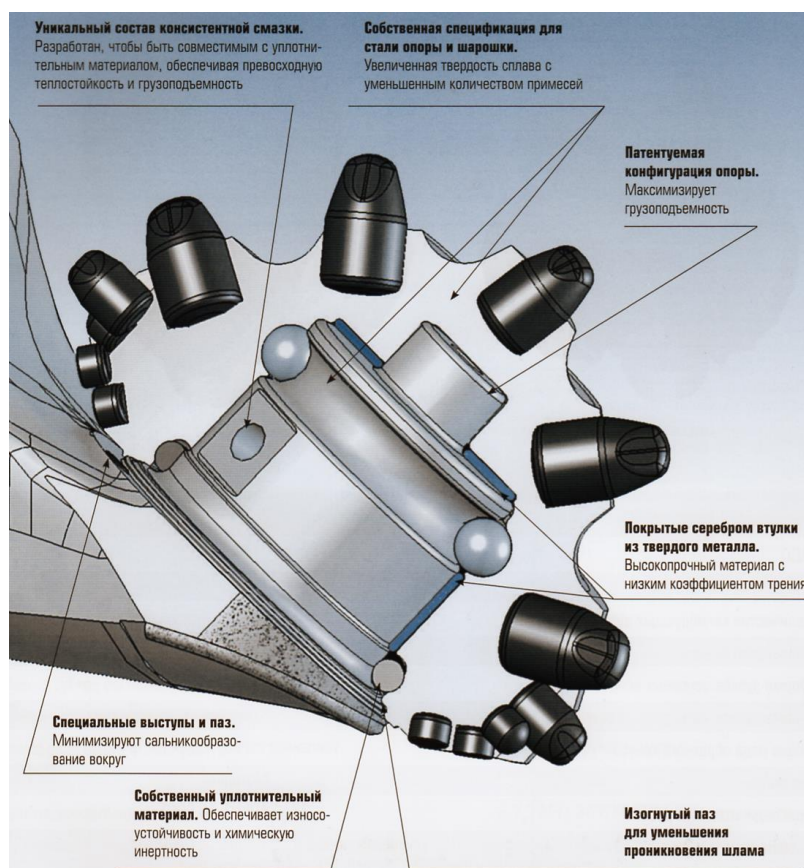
Конструкция опоры трехшарошечного долота 215,9Z45RD1SD – герметизированный подшипник скольжения с твердосплавными зубками на обратном конусе шарошки
